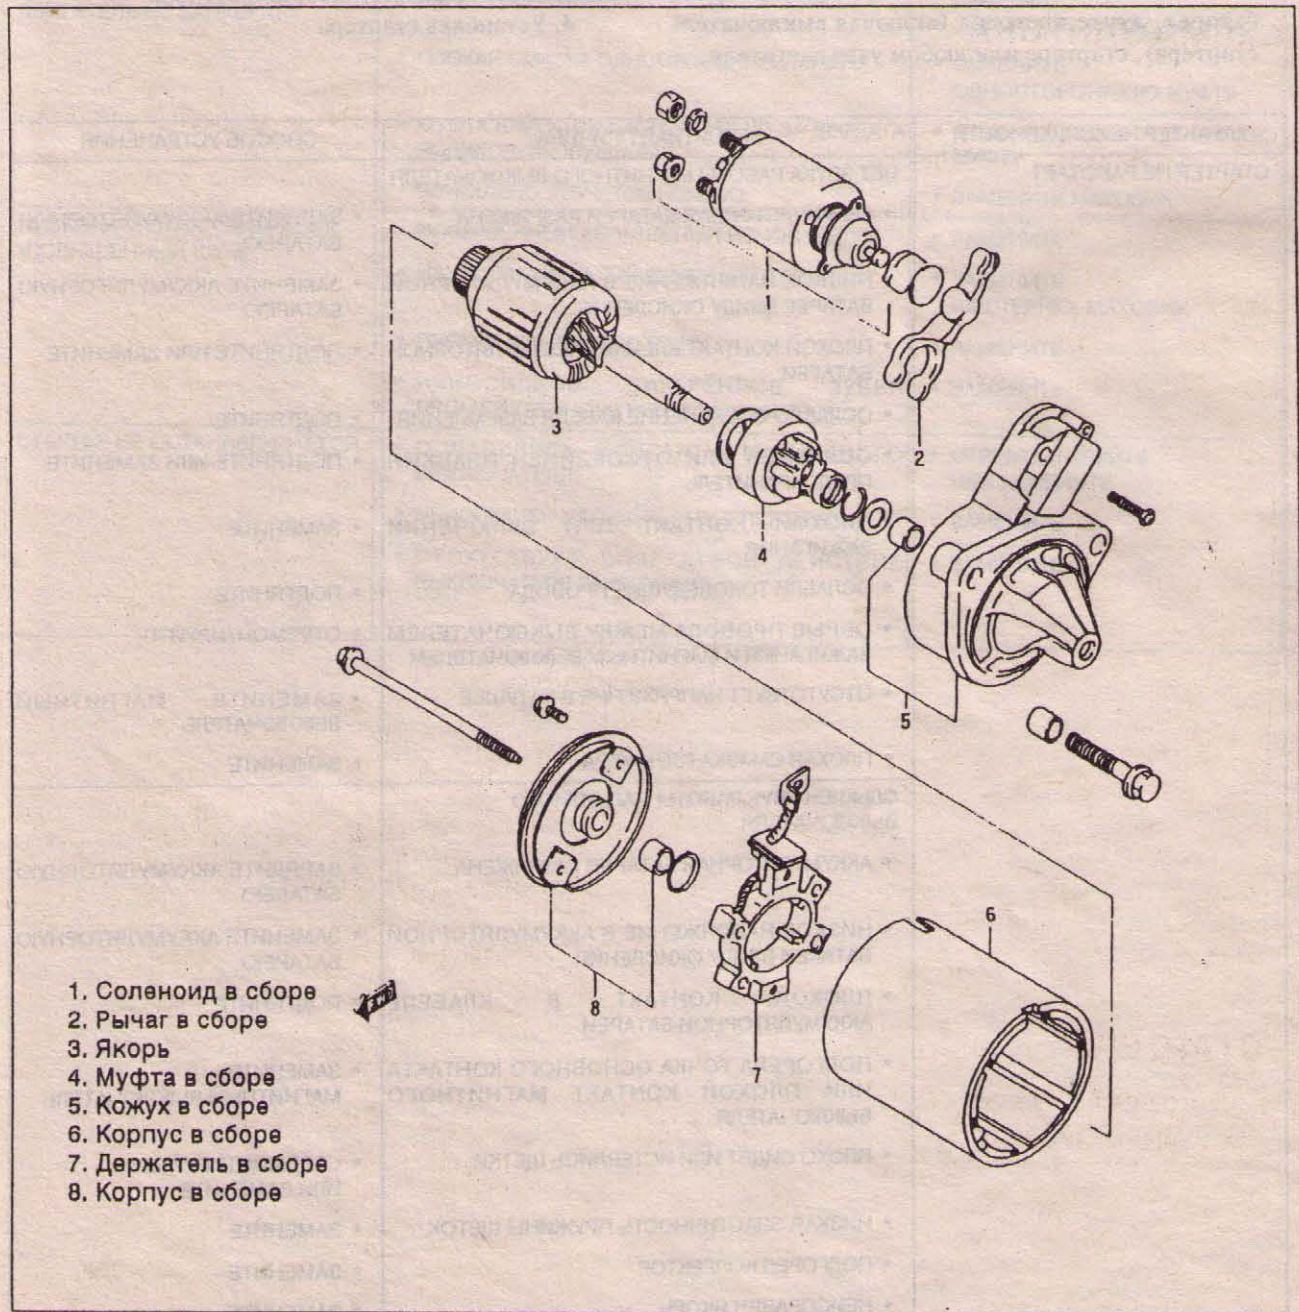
F—2 СХЕМА КОМПОНОВКИ СТАРТЕРА
